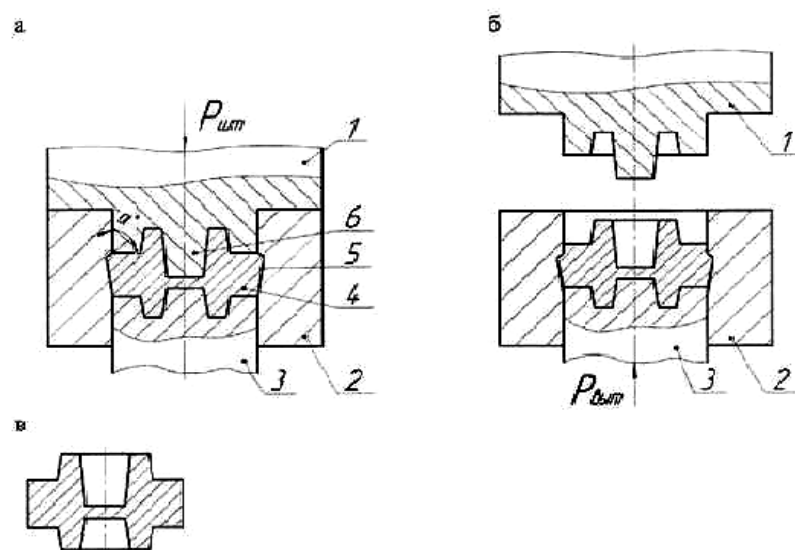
Схема штамповки изделия без штамповочных уклонов: а – момент окончания формообразования полуфабриката; б – момент выталкивания полуфабриката; в – поковка.. 1 – верхняя часть штампа; 2 – нижняя часть штампа; 3 – выталкиватель; 4 – полуфабрикат; 5 – боковая стенка полуфабриката с двухсторонними уклонами; 6 – штамповый знак
